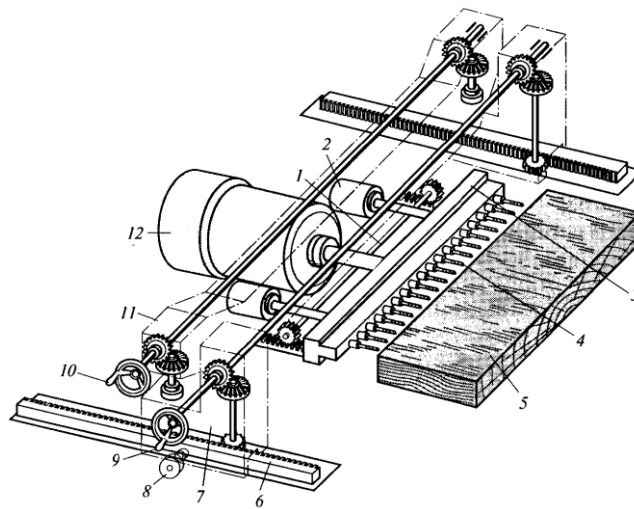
Свердлильний агрегат багатошпindelного верстата: 1 – вал; 2 – пневмоциліндр; 3 – шпindelна насадка; 4 – шпindel; 5 – деталь; 6 – напрямна; 7 – супорт; 8 – фіксатор; 9, 10 – маховички; 11 – траверса; 12 – електродвигун
